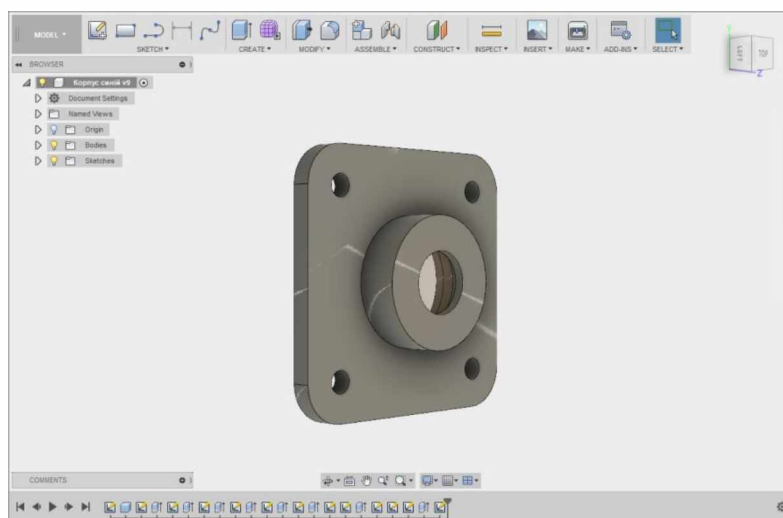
Графічна модель швидкозношуваної деталі (корпус підшипника)
